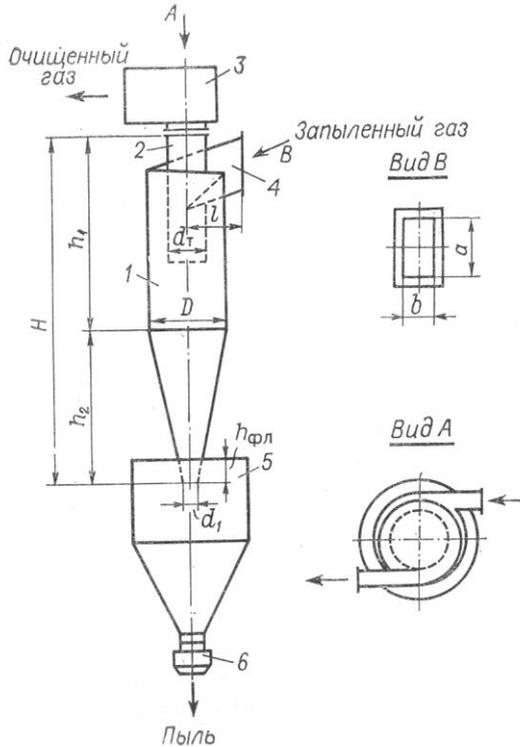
Возвратно-проточный циклон: 1- корпус; 2- выхлопная труба; 3- улитка; 4- входной патрубок; 5- бункер; 6- затвор для выгрузки пыли
